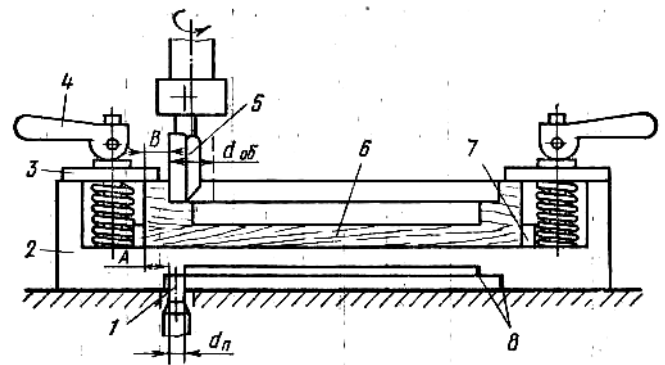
Схема обработки детали в шаблоне на фрезерном станке с верхним расположением шпинделя:
